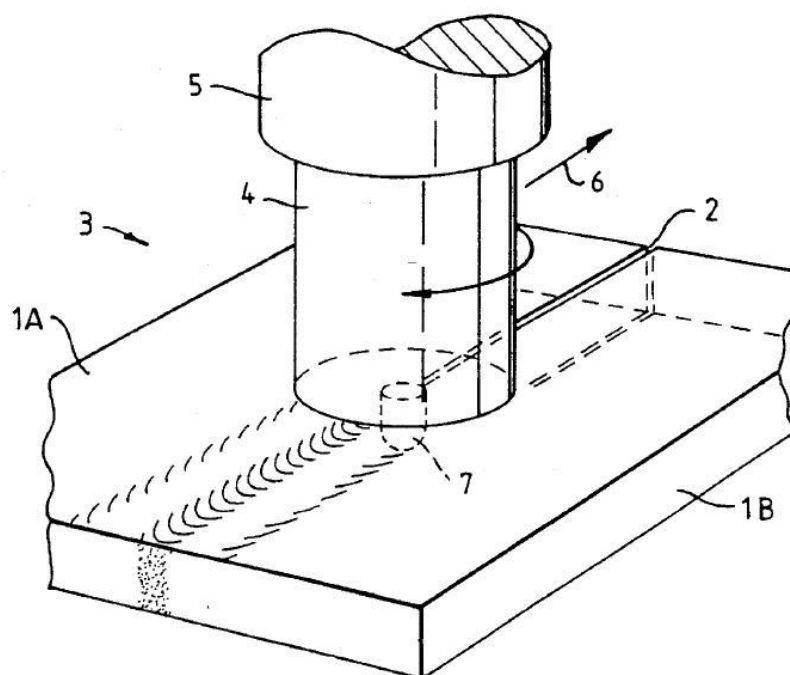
Vista isométrica do processo de solda por fricção e mistura.
